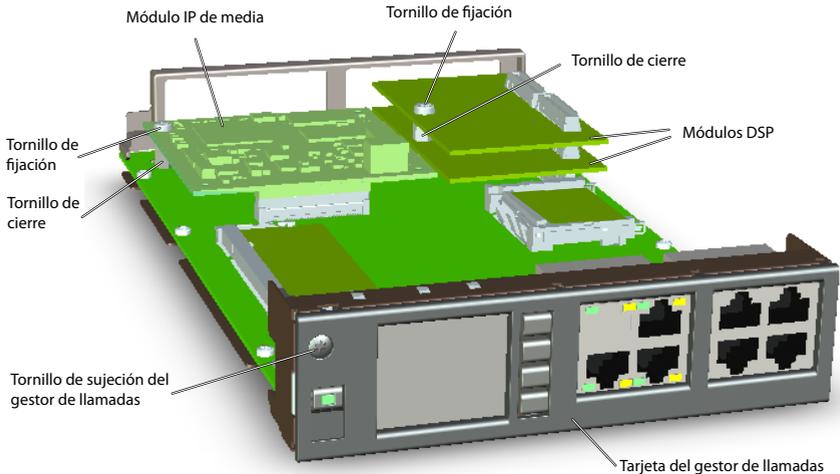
Módulos de sistema en la tarjeta gestor de llamadas
